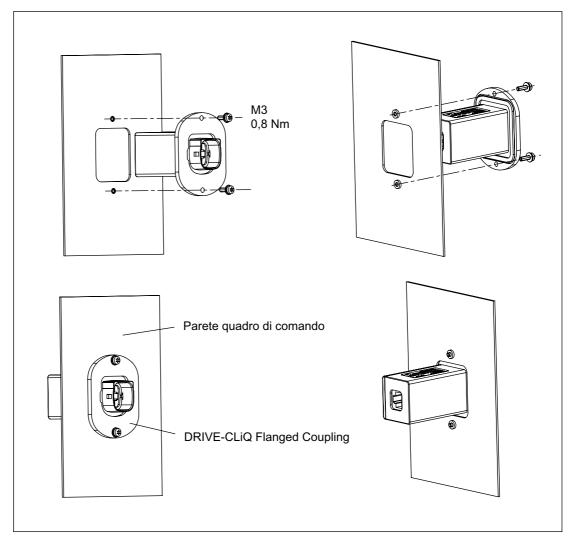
DRIVE-CLiQ Flanged Coupling
